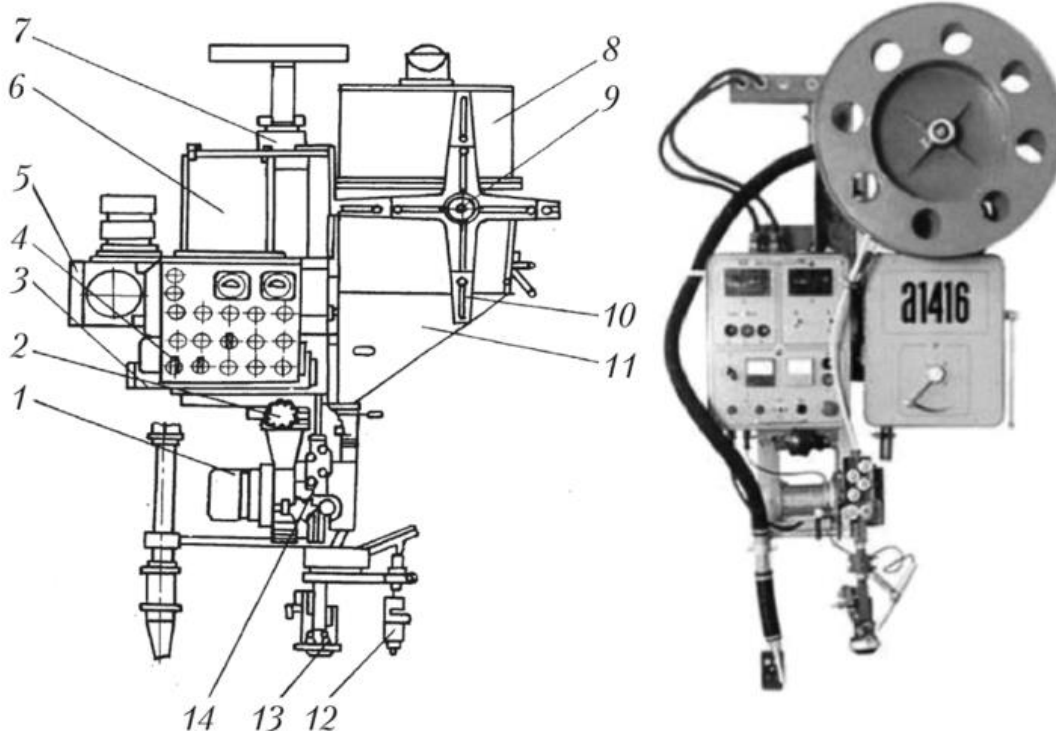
Конструкция (а) и внешний вид (б) самоходной сварочной головки
